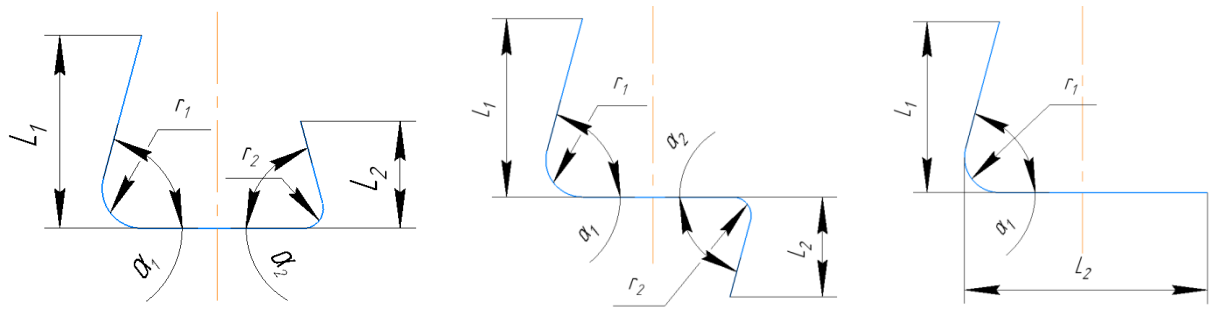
Схема деталей, изготавливаемых двухугловой гибкой
